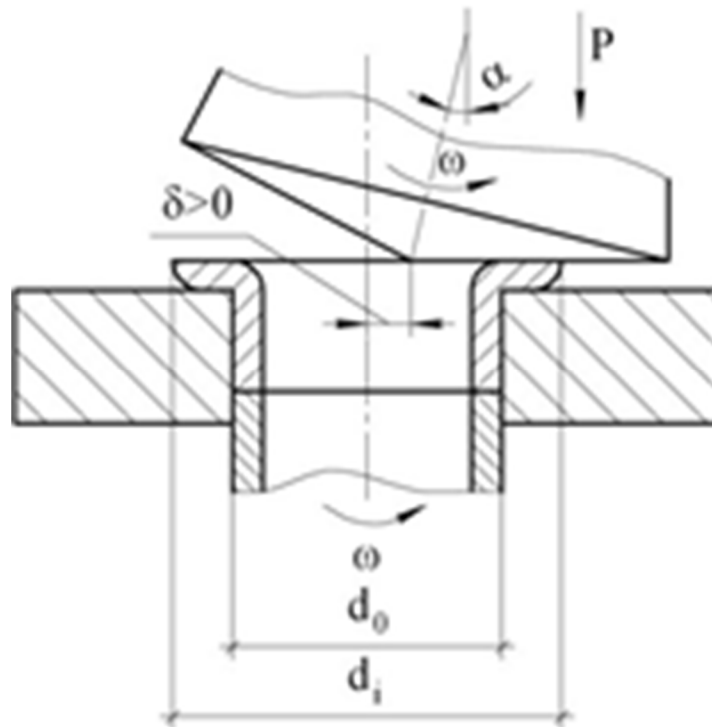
Технологічна схема формування зовнішнього фланця заготовки під час штампування обкочуванням.
